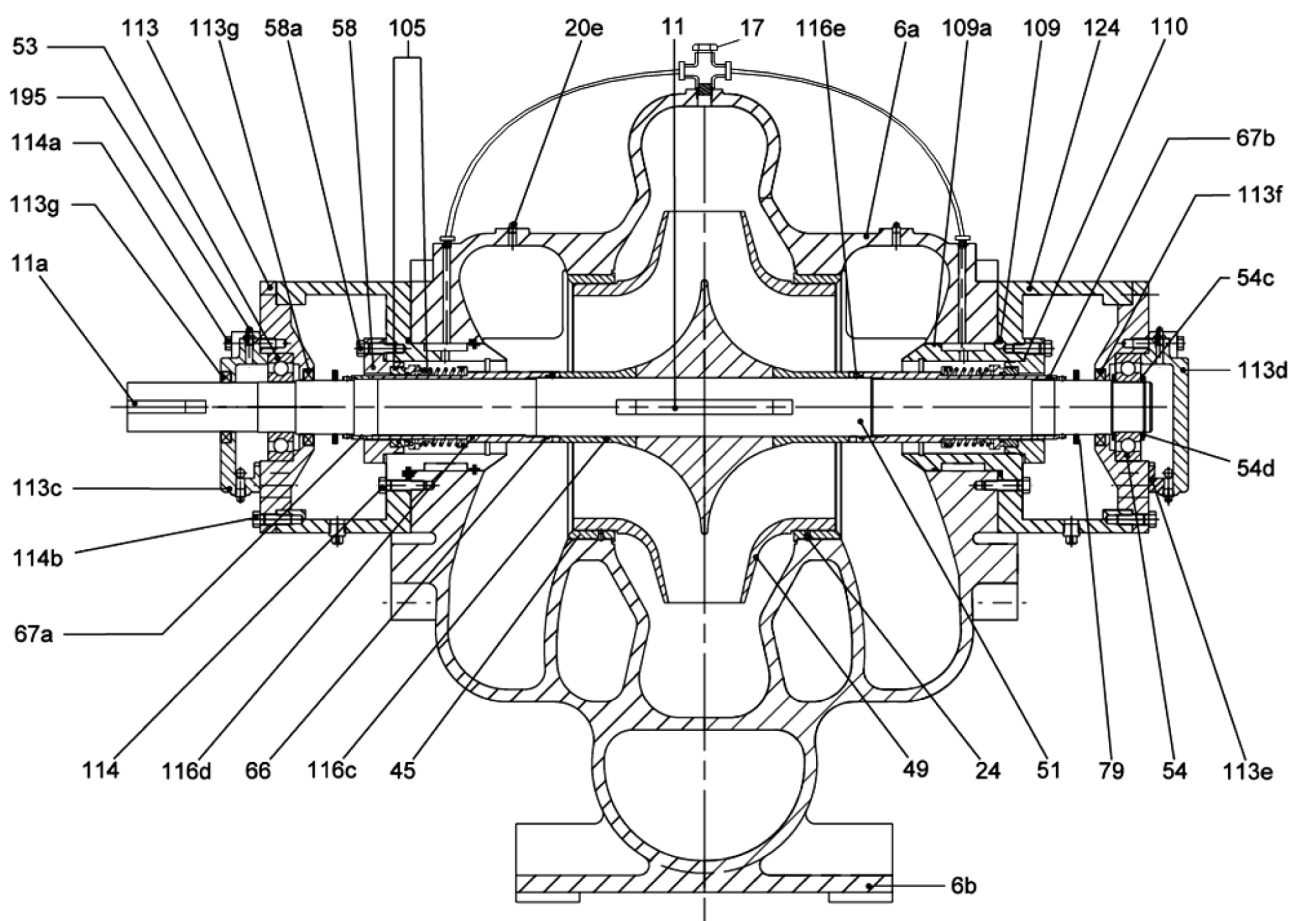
Вид в разрезе, тип конструкции 4, с торцевыми уплотнениями вала
